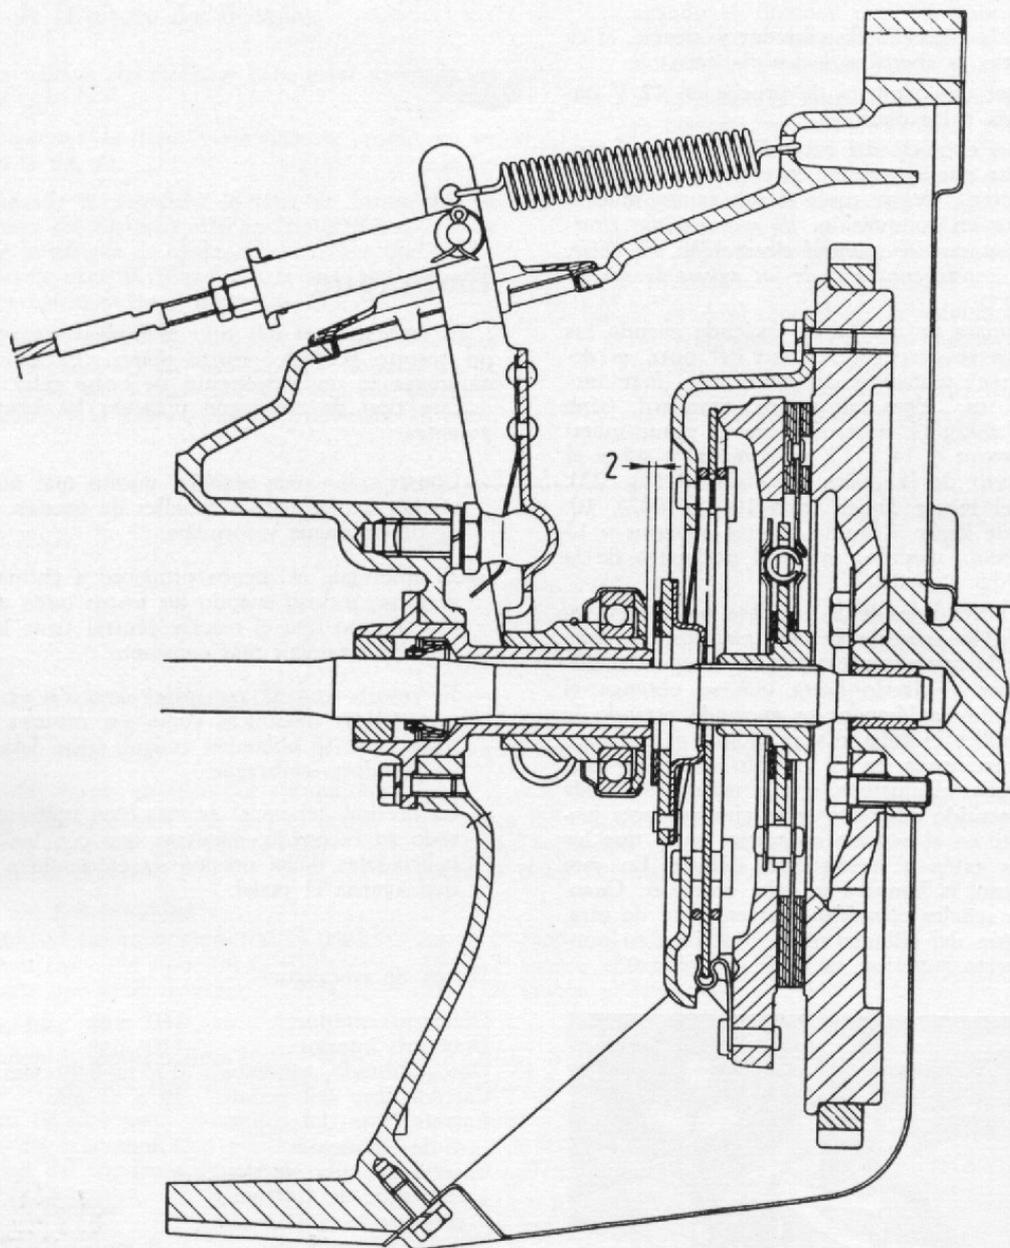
Sección en el embrague. La medida «2 mm.» indica la carrera libre del cojinete de desembrague
